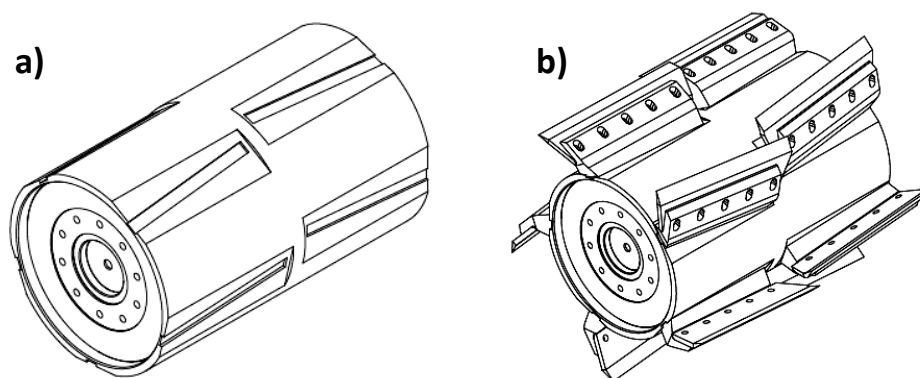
; Tamburo rotore sperimentale; rotore CRA-ING (b)
